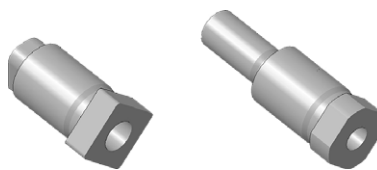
AYUDA DE POSICIONAMIENTO INSERTADA (IZQUIERDA) Y AYUDA DE POSICIONAMIENTO ATORNILLADA
